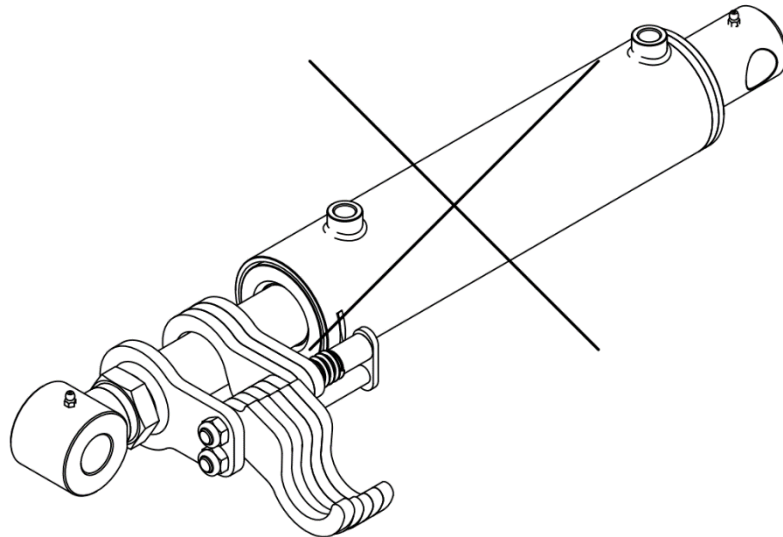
Cliquets mal montés sur la tige du piston du vérin. L'omission partielle de la fixation des cliquets au vérin entraîne une répartition inégale des forces agissant sur la tige du piston et peut conduire à un flambage de la tige du piston et endommager l'ensemble du vérin. Une telle installation des cliquets est inadmissible !
